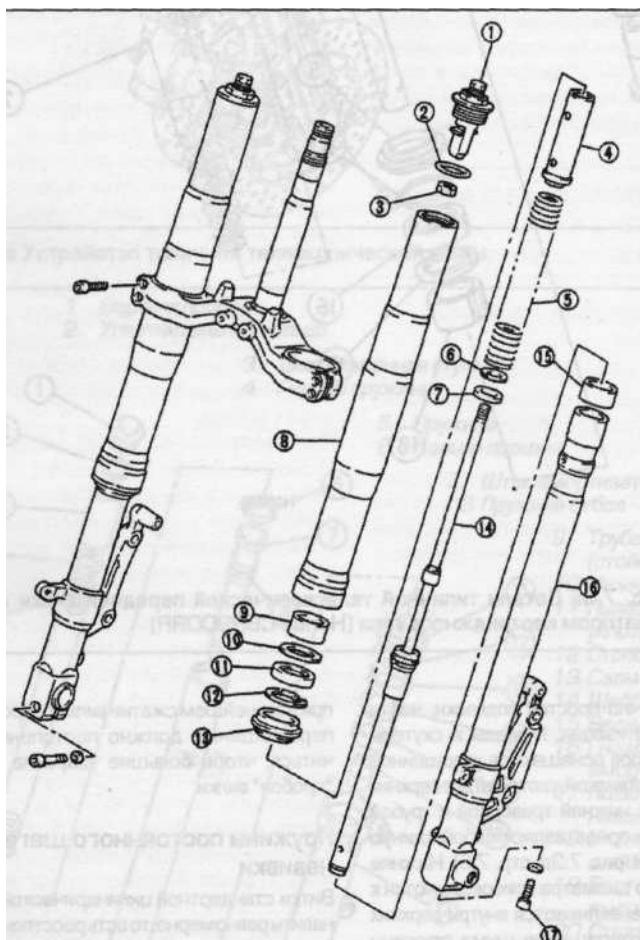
г Детали типичной перевернутой телескопической передней вилки с амортизатором картриджного типа (Yamaha YZF750R)
